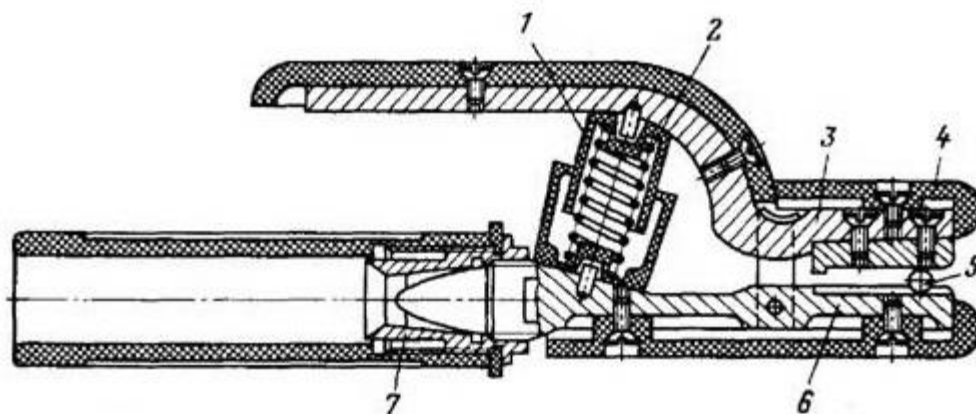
Электродержатель пассатижный: 1 — защитный колпачок пружины; 2 — пружина; 3 - рычаг с верхней губкой; 4 - теплоизоляционная защита; 5 - электрод; 6 - нижняя губка; 7 - конус резьбовой втулки.
